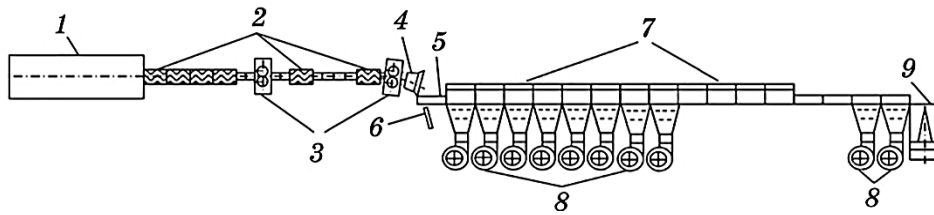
Схема розташування основного обладнання сучасної Стелмор-лінії [62]: чистовий вальцювальний блок (1); ділянка водяного охолодження (2); трайбапарати (3); виткоутворювач (4); приймальний стіл витків вальцівки (5); пірометер (6); ділянка регульованого повітряного охолодження з вальцевим транспортером і теплоізоляційними кришками (7); дуттьові повітряні вентиляторні системи (8); шахта виткозбірника (9).
